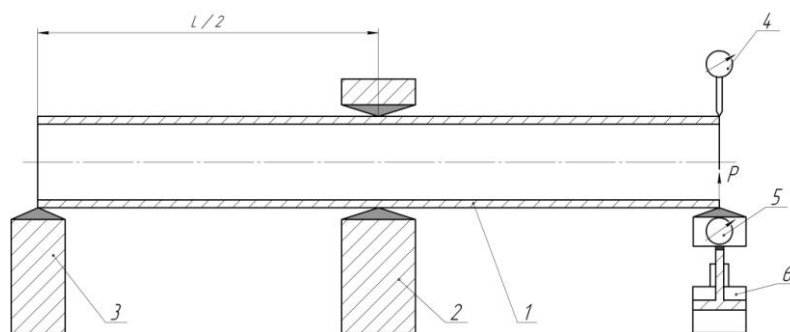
Принципова схема тарувального стенда корпусу пристрою
